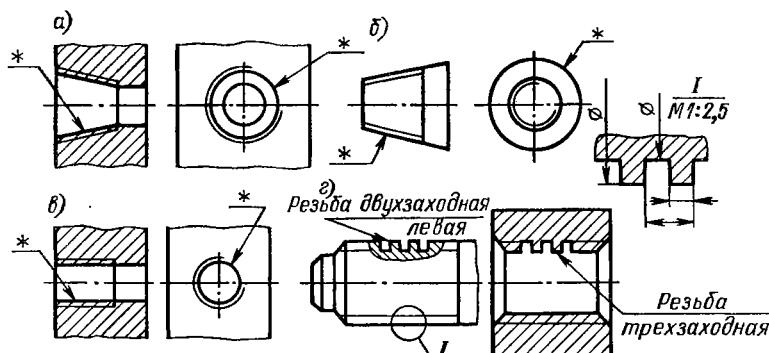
Места нанесения обозначения резьб: а – конической; б – цилиндрической трубной; г – прямоугольной
